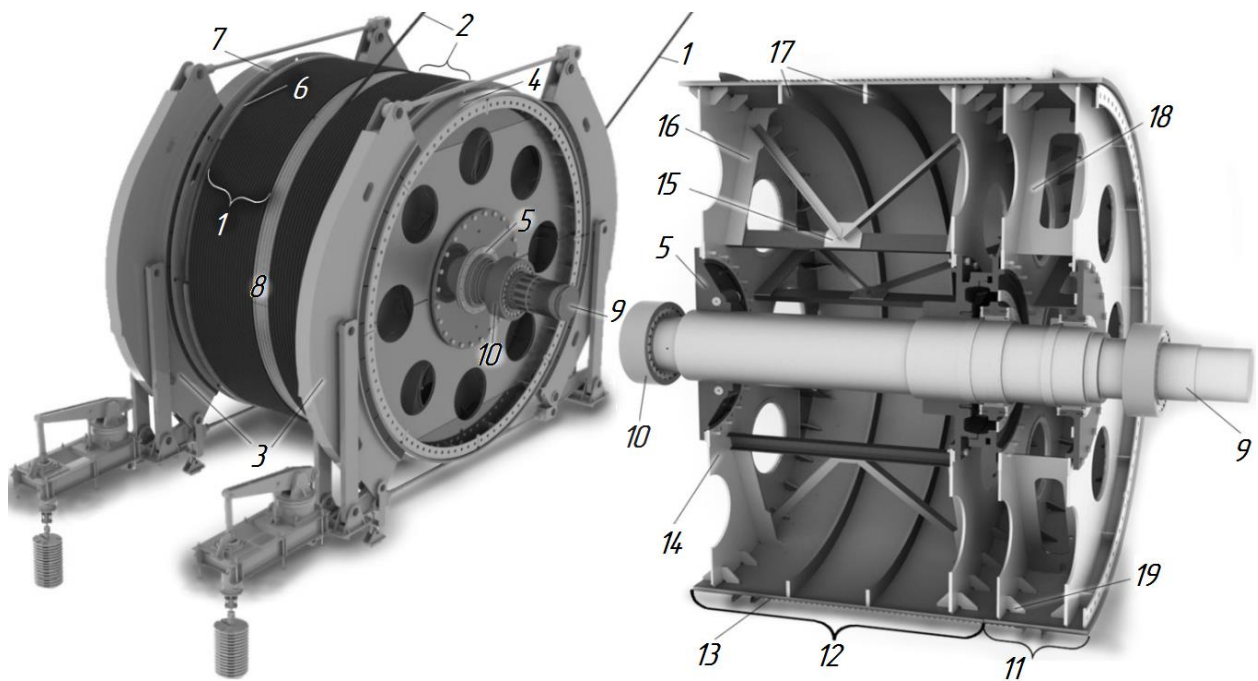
Общий вид и разрез барабана ШПМ типа ЦР:
